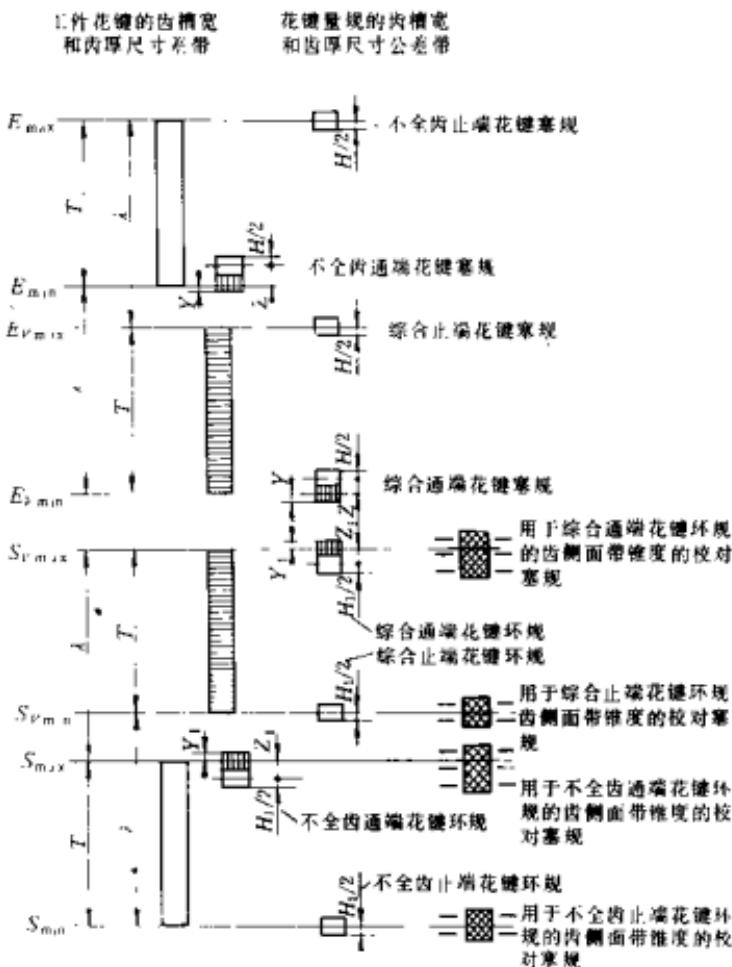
花键量规的齿厚和齿槽宽尺寸公差带
